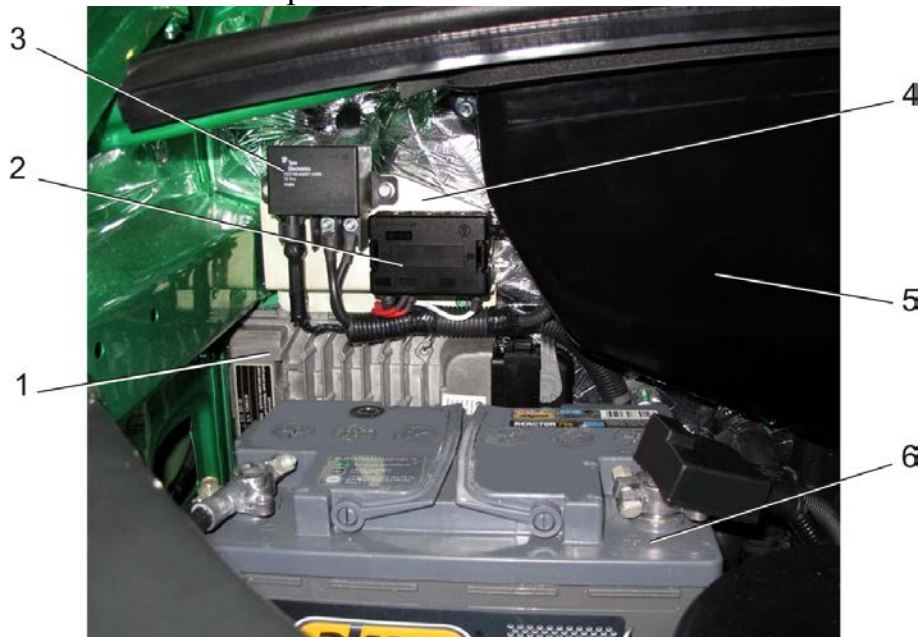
Установка блока управления двигателем: 1 – блок управления двигателем; 2 - блок предохранителей; 3 – реле нагревателя воздуха; 4 – кронштейн; 5 – короб воздухозаборника передний; 6 – аккумуляторная батарея
